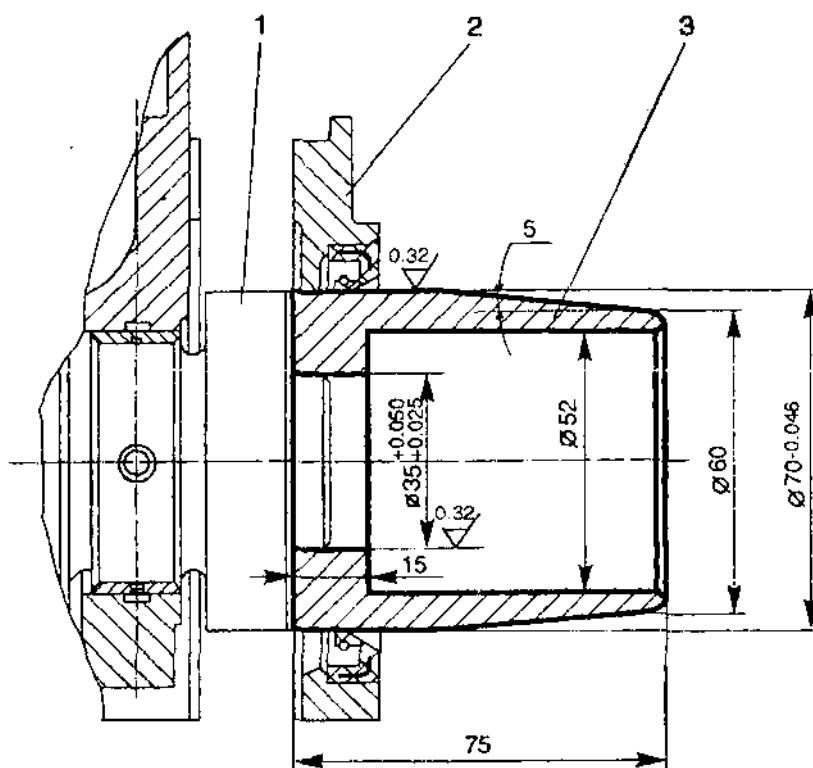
Установка держателя манжеты на фланец коленчатого вала:
